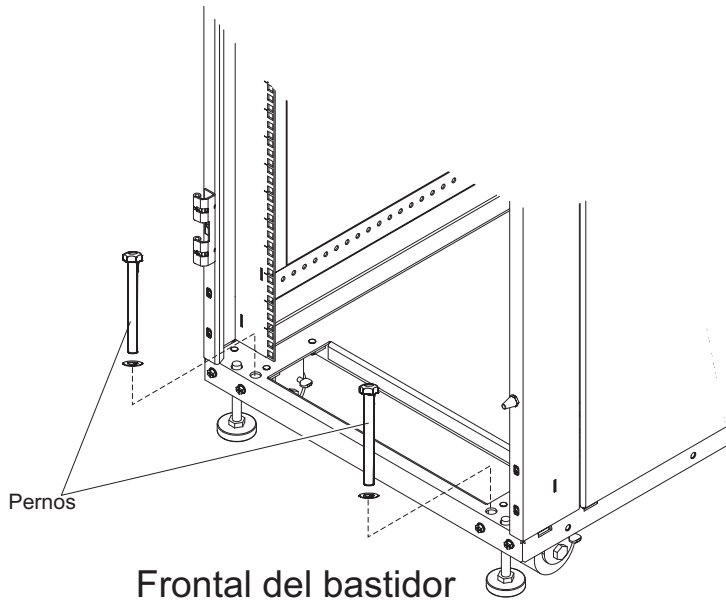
Atornillado de la parte frontal del bastidor a la superficie del suelo
